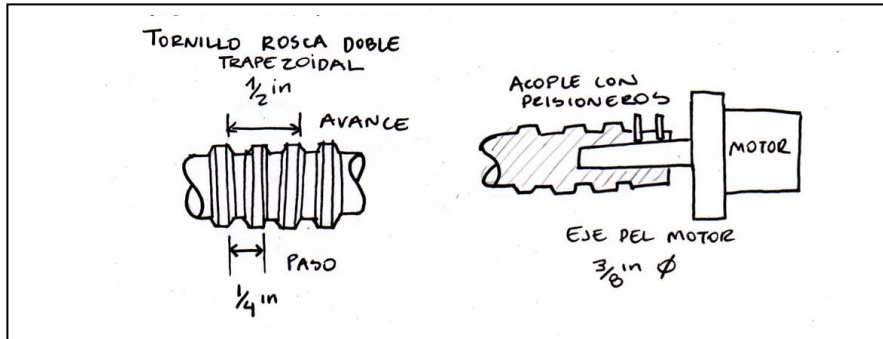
Boceto posibles dimensiones y acople motor del tornillo sinfín
